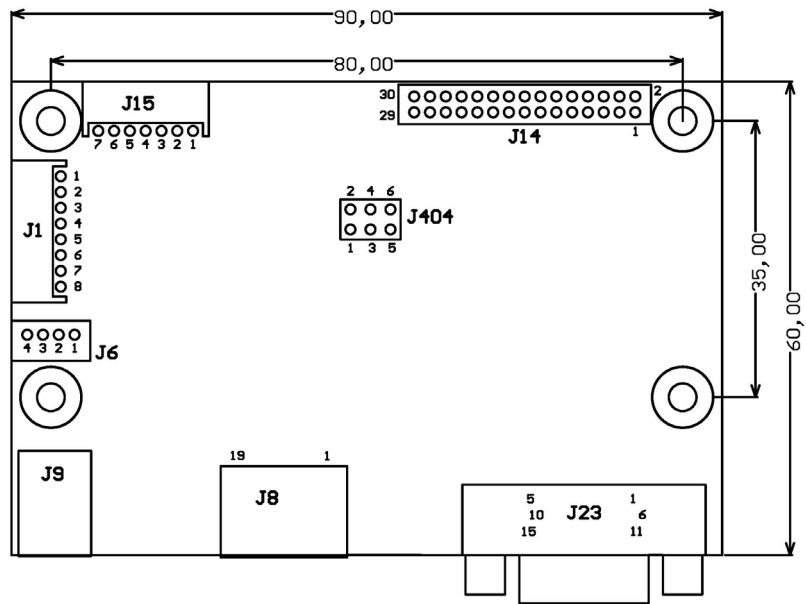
Габаритный чертёж контроллера УКМ-1912-02
